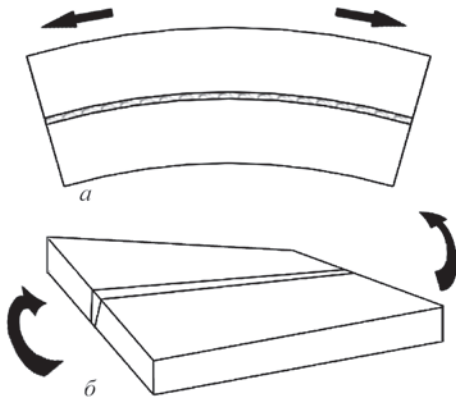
Схемы возможного макродеформирования сварной пластины при сварке, которое может вызывать локальное увеличение растягивающих напряжений: *a* — изгиб; *б* — кручение
